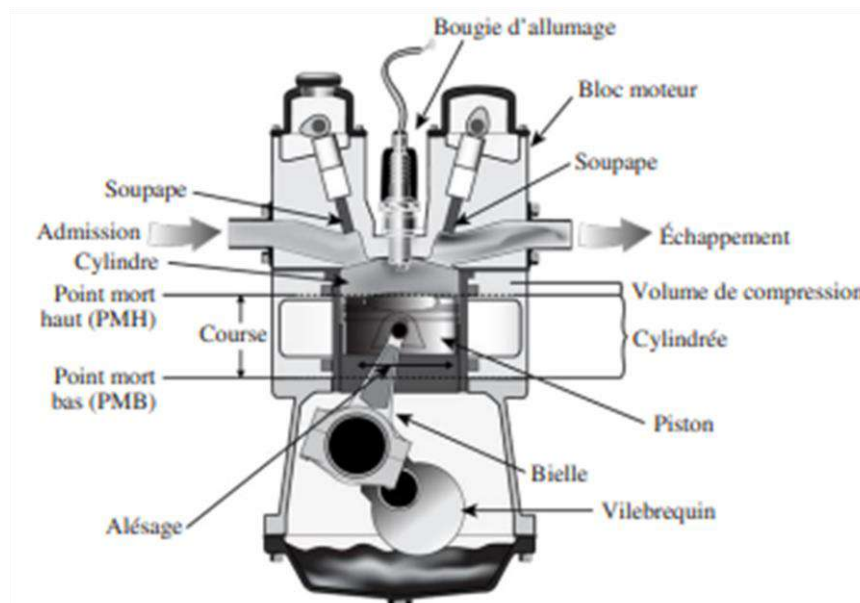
Principaux éléments du moteur à combustion interne.
